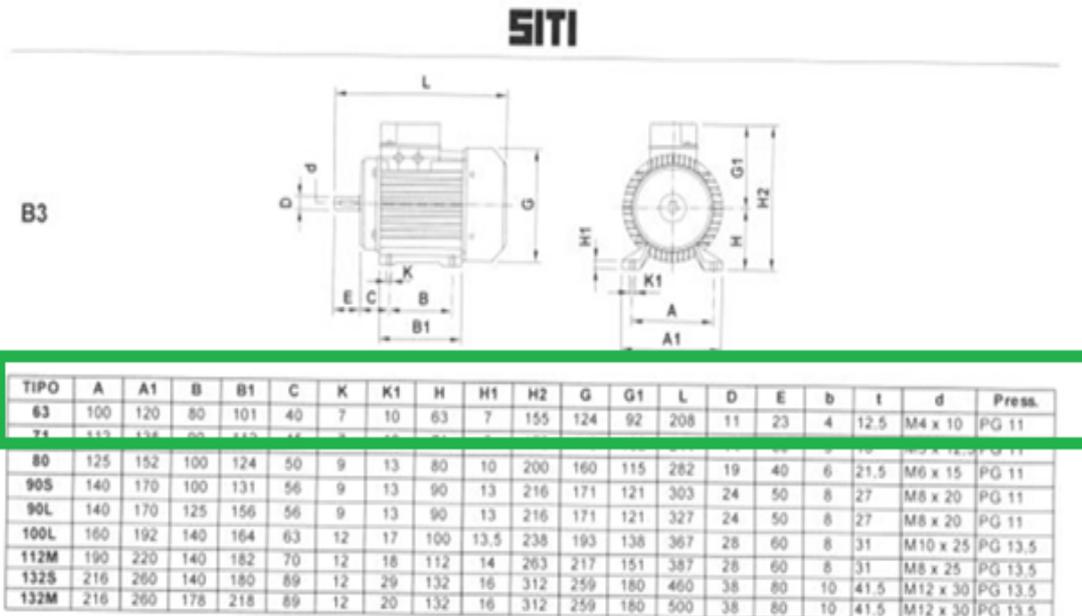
Dimensiones motor para calibración de grosor de paso del cuero
